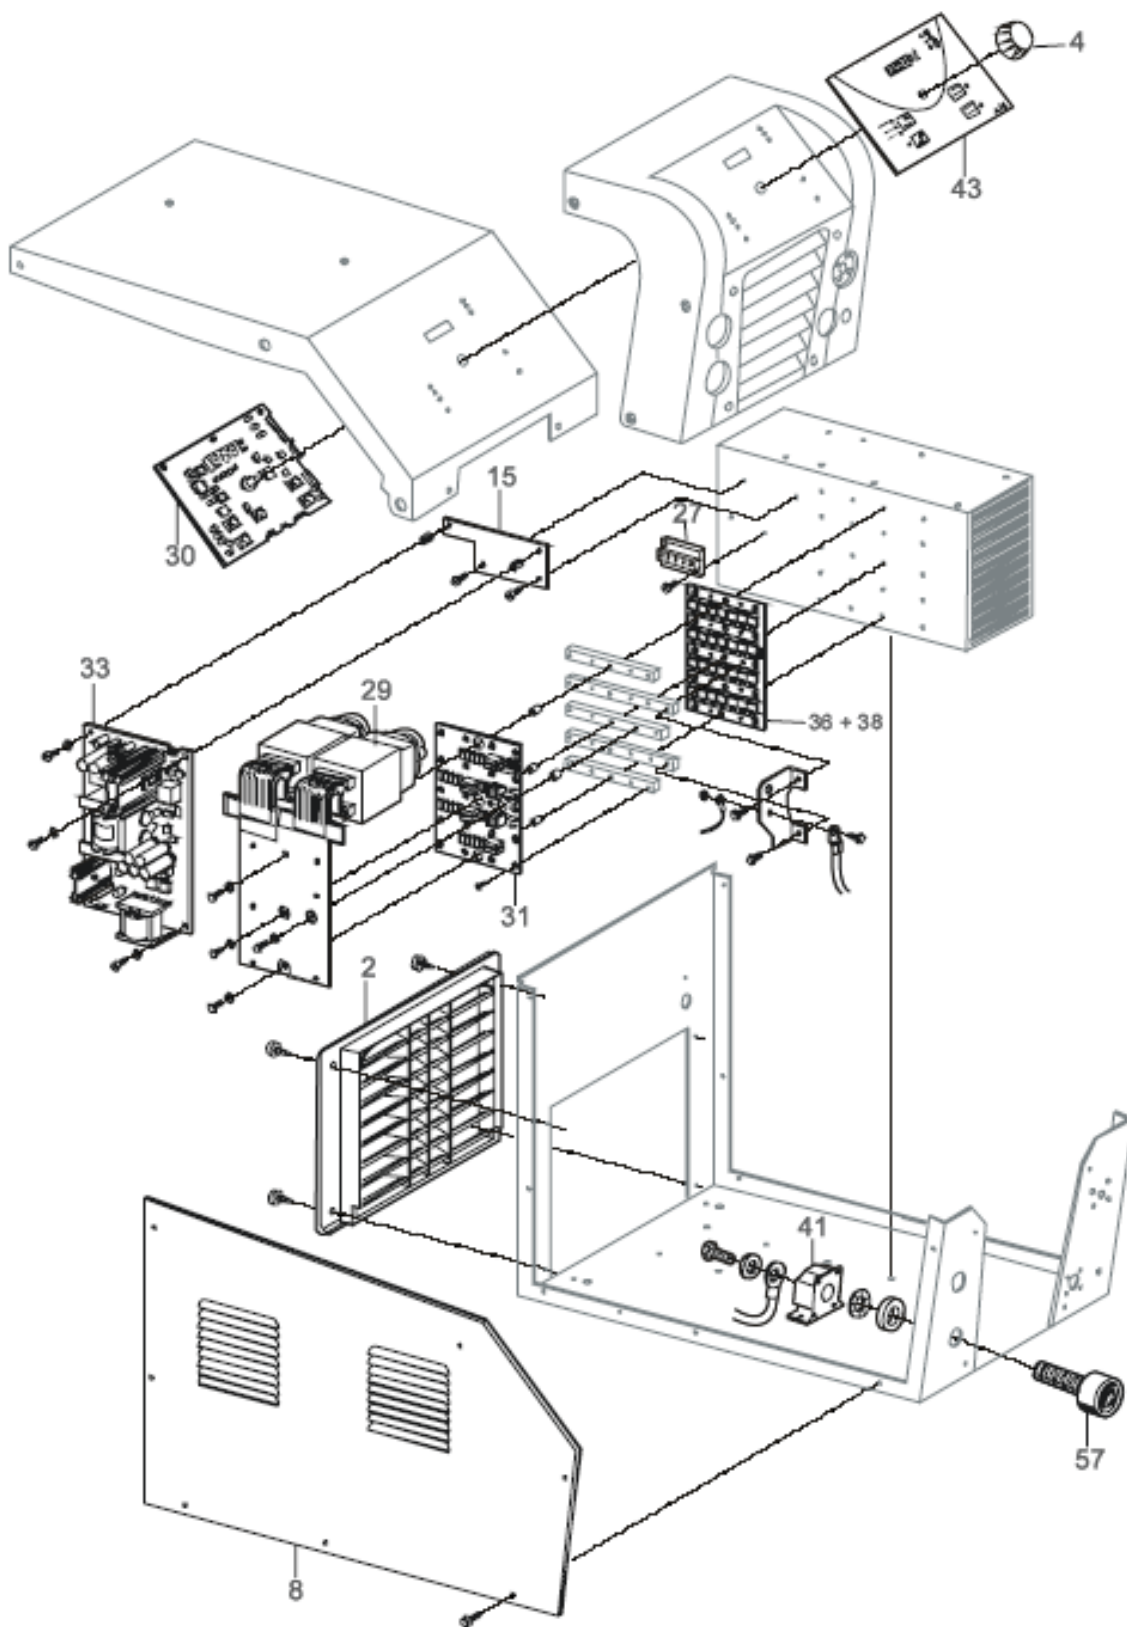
Explosietekening RODIE 250 - 320 (links)
